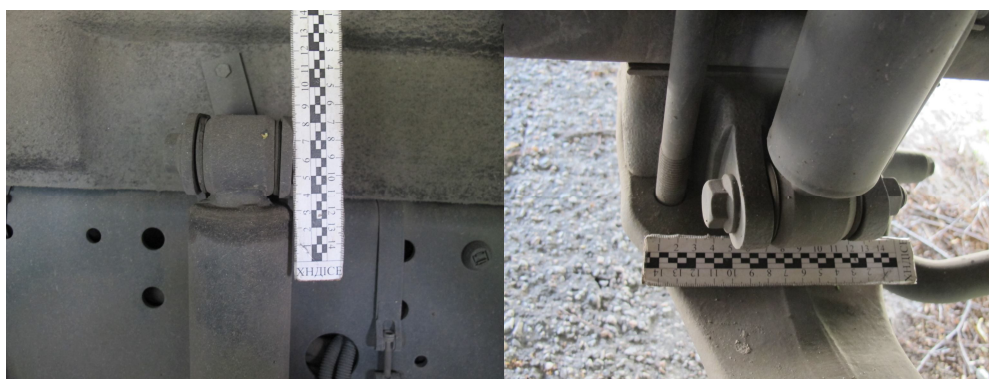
Детальний вид верхнього та нижнього кріплення амортизатора правого переднього колеса автомобіля MAN TGM
